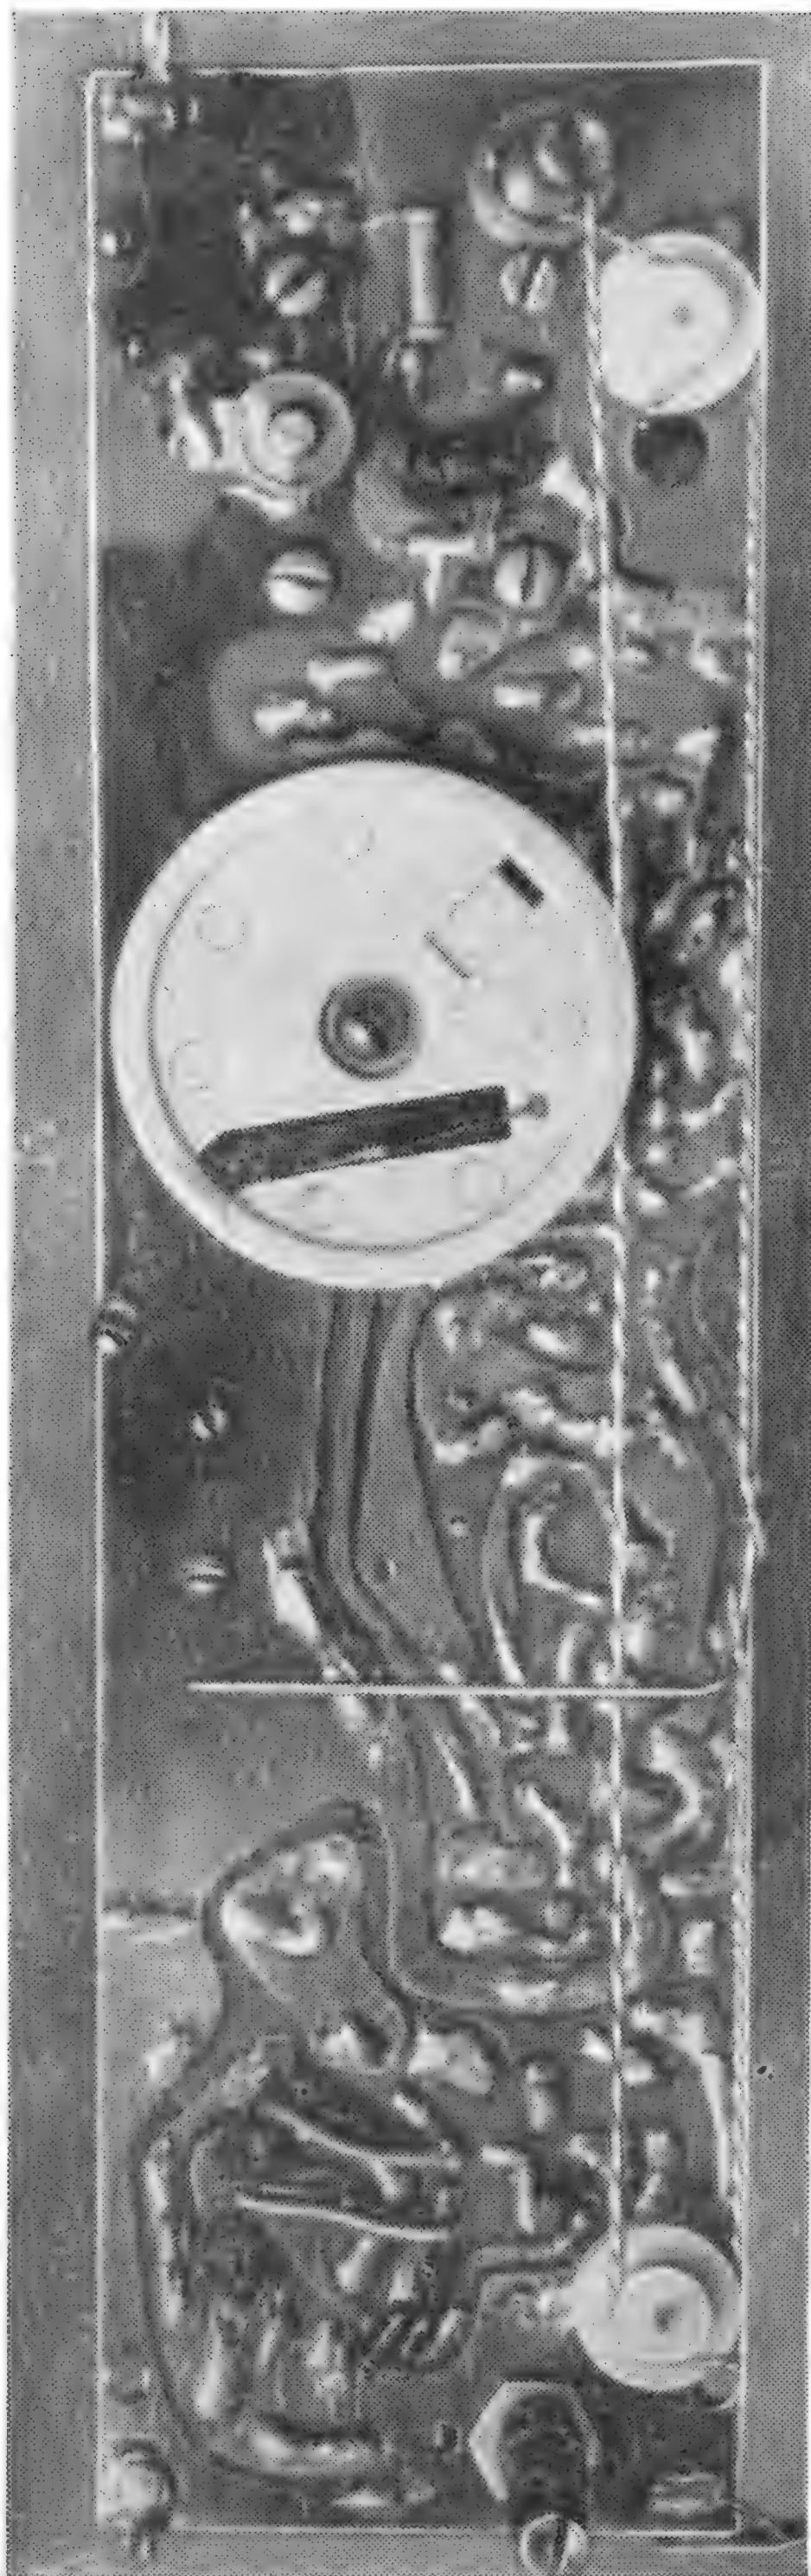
Размещение деталей шкально-верньерного механизма на печатной плате.
